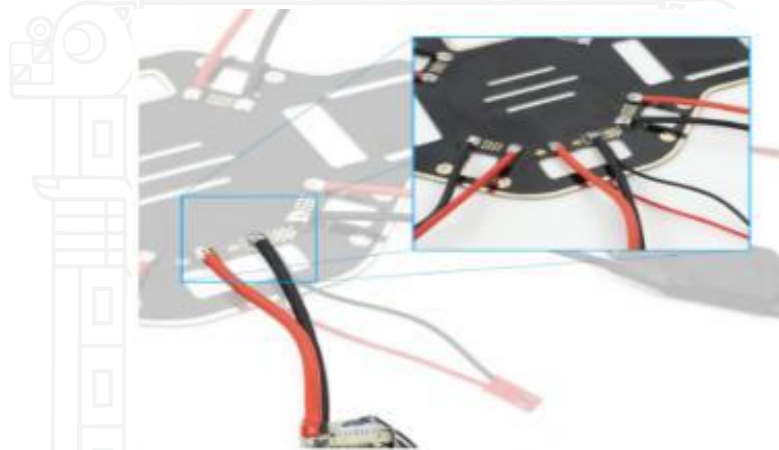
Soldado del módulo y ESC a la placa del F450
